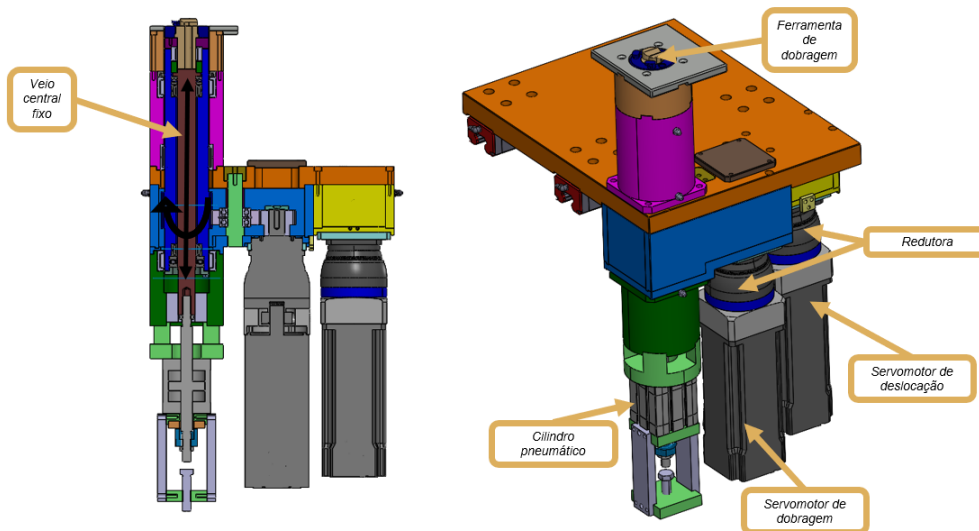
Dispositivo de dobragem CNC do equipamento de dobragem
